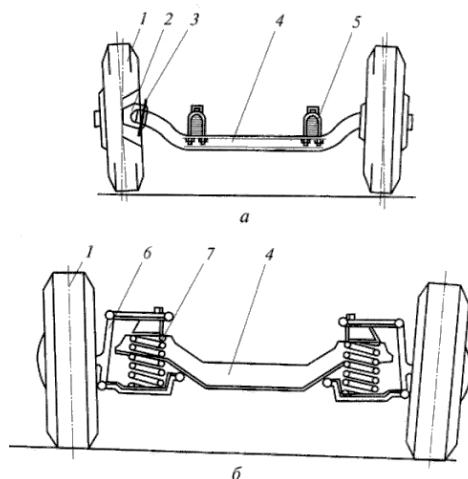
Передние управляемые мосты: *а* — с неразрезной балкой; *б* — с разрезной балкой; 1 — колеса; 2 — поворотная цапфа; 3 — поворотный шкворень; 4 — балка; 5 — рессора; 6 — стойка; 7 — пружина подвески
